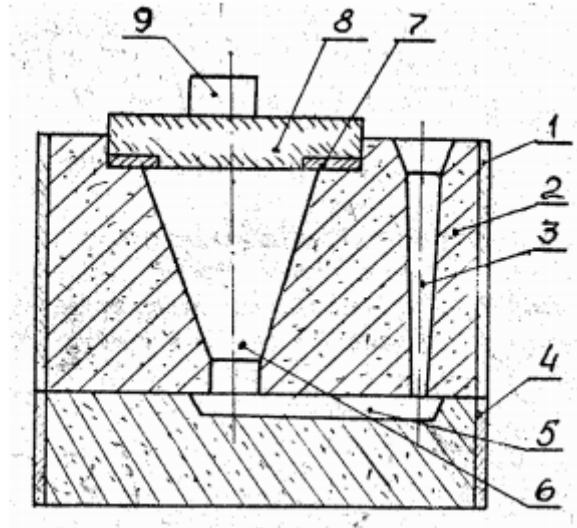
Форма для одержання конусної проби при визначенні об'ємної усадки сплавів 1, 4 - опоки; 2 - суміш; 3 - стояк; 5 – ливниковий хід; 6 – порожнина форми; 7 - холодильник; 8 - стрижень; 9 – вантаж.
